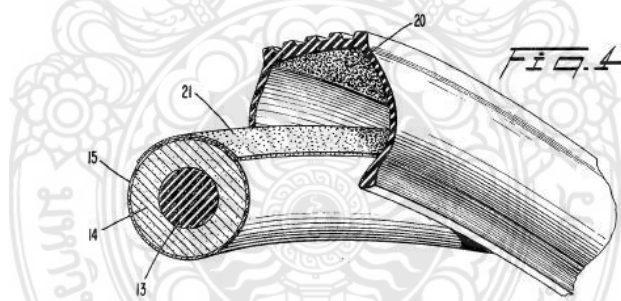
ล้อยางแบบ Run-flat assembly [51]
